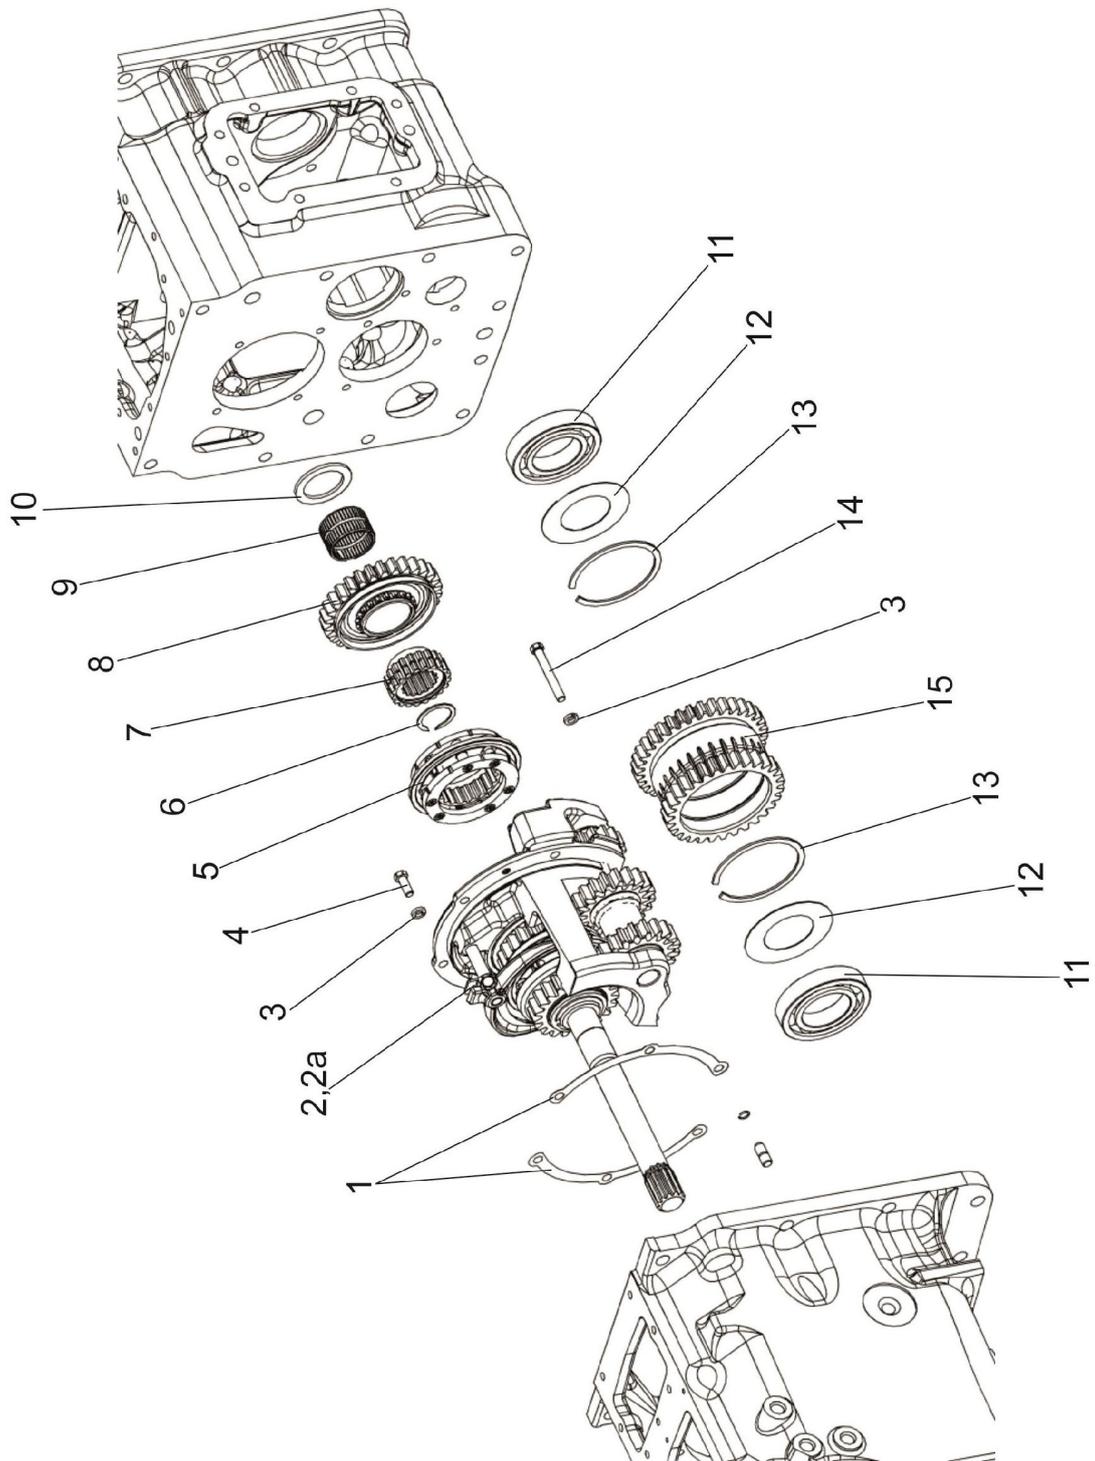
Синхронизированный реверс-редуктор со встроенным редуктором
